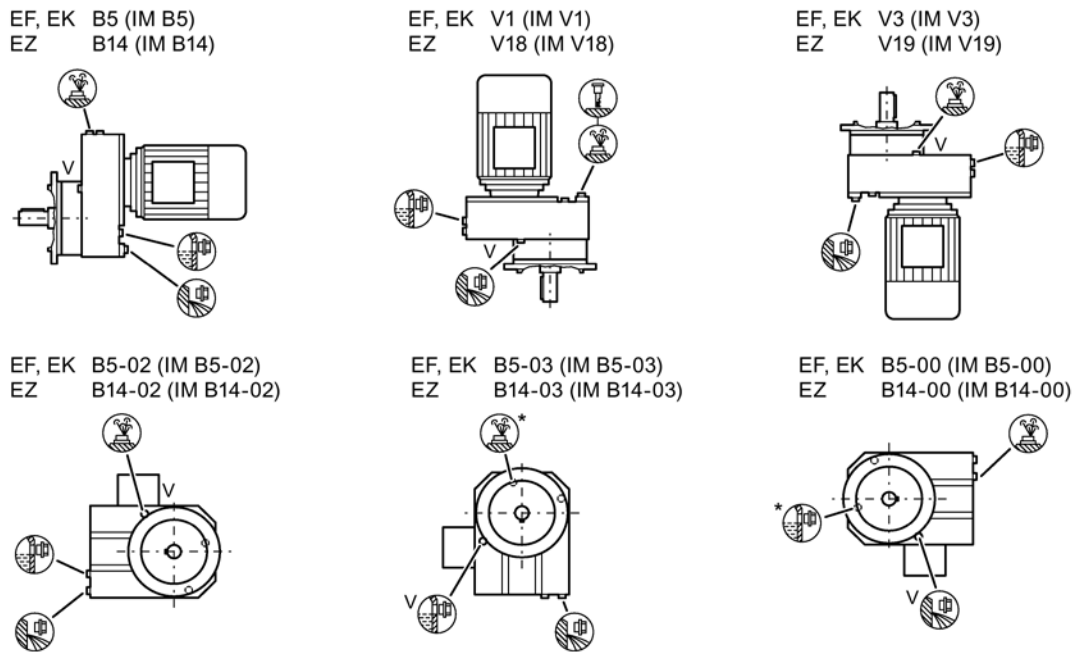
Bauformen für E. Baugrößen 38 - 148
